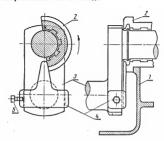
Выпрессовка корпуса коренного подпинника: 1 — рама динтеля; 2 — корпус подпинника; 3 — коленчатый вал; 6 — приспособление; 5 — стопорый бол.
